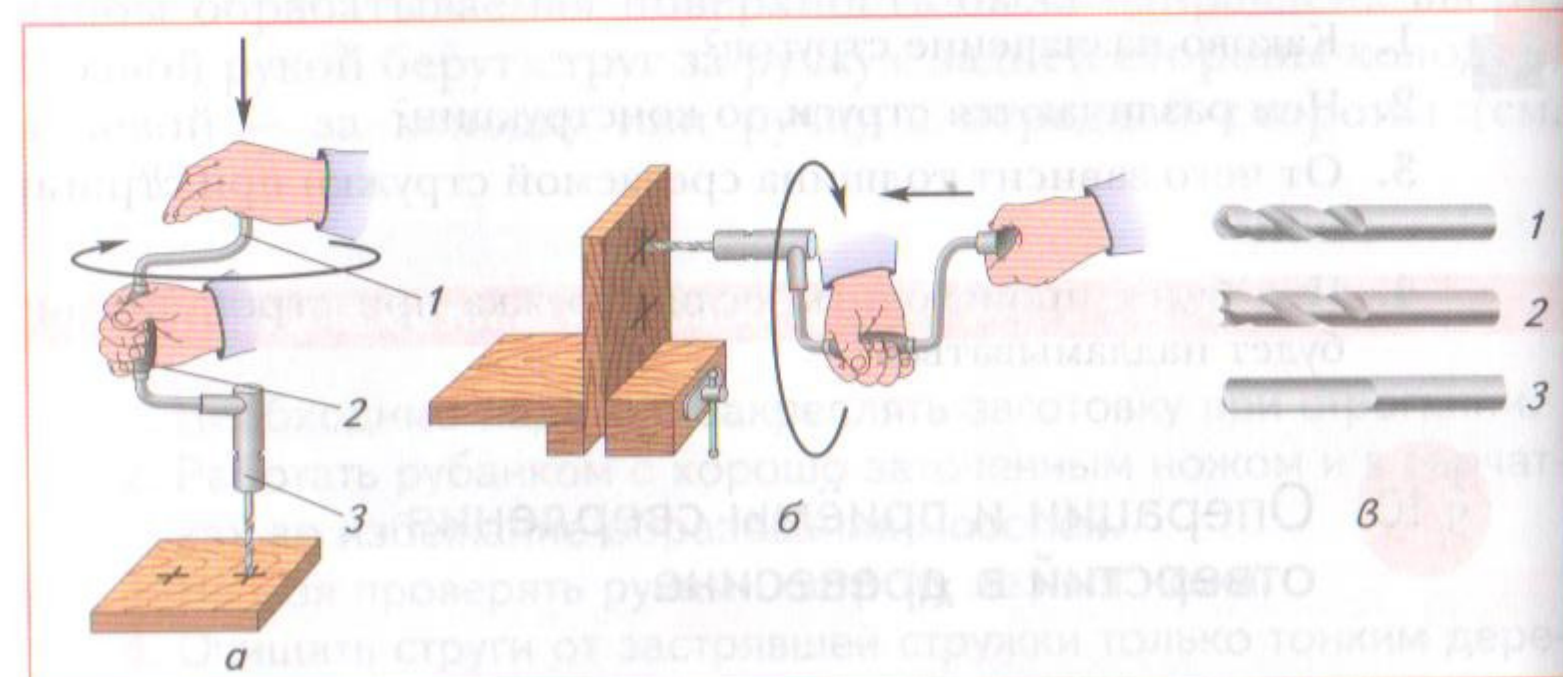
Сверление коловоротом: а — на подставке: 1 — упор; 2 — рукоятка вращения; 3 — патрон со сверлом; б — в зажиме верстака (например, столярного); в — свёрла: 1 — винтовое; 2 — центровое; 3 — ложечное
